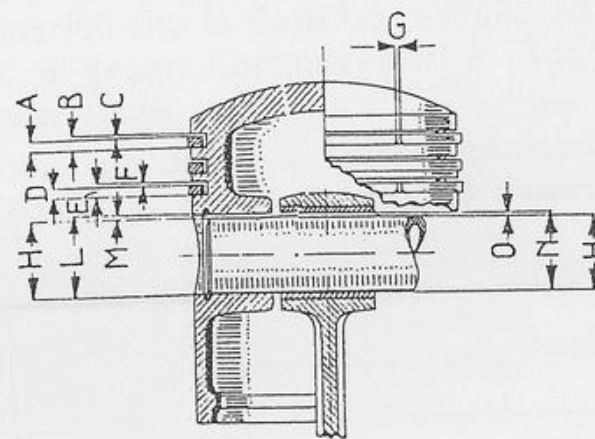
Pistone - Spinotto - Fasce elastiche.
